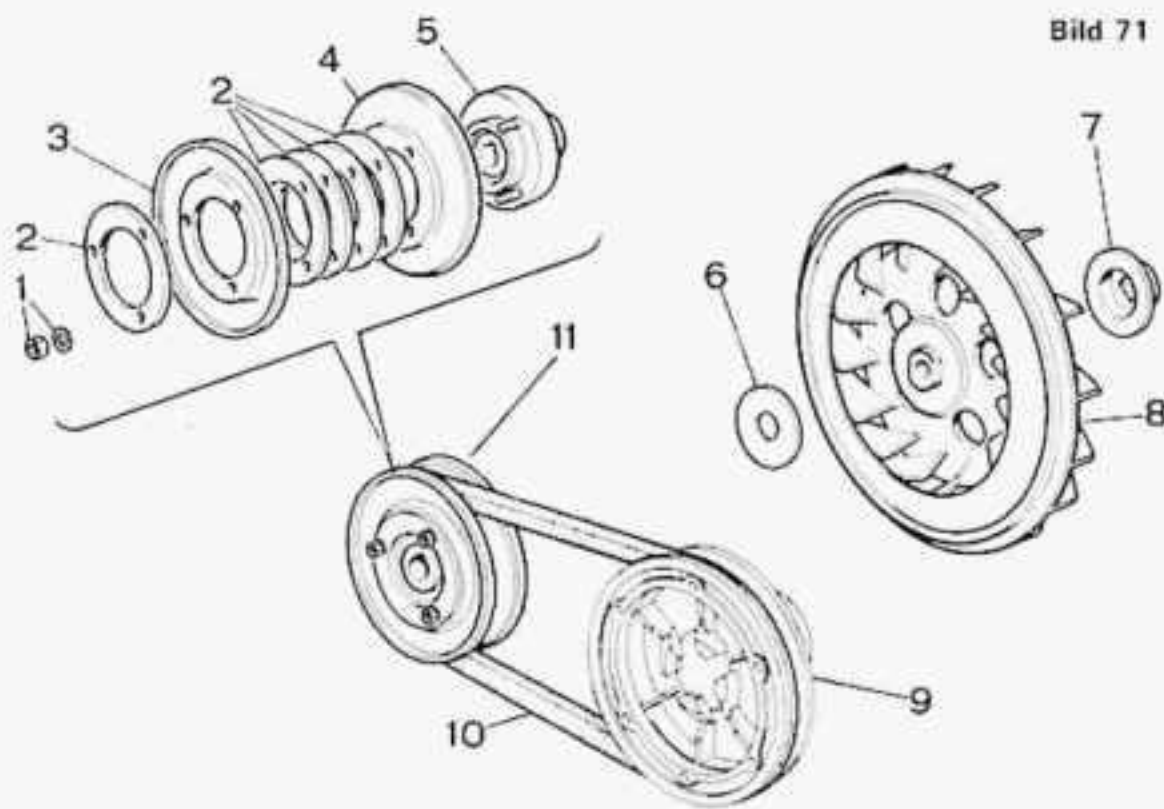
Antrieb von Lichtmaschine und Kühlgebläse mit Vorrichtung zum Einstellen der Keilriemenspannung
